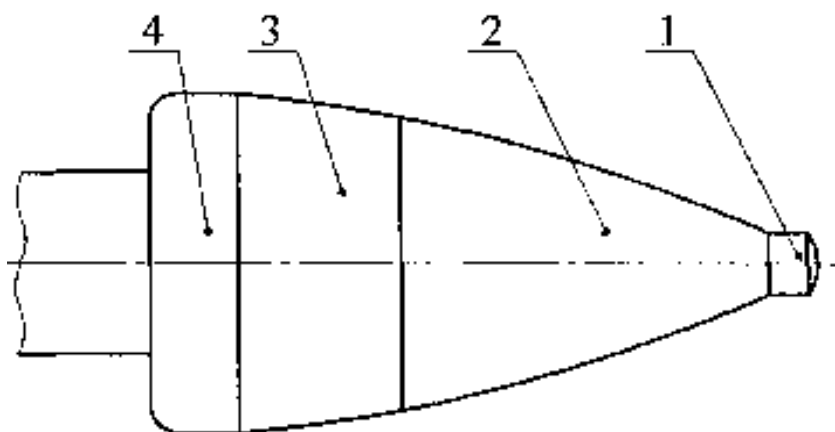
Оправка прошивного стана с носиком: 1 – носик оправки; 2 – рабочий конус; 3 – конус поперечной раскатки; 4 – обратный конус
